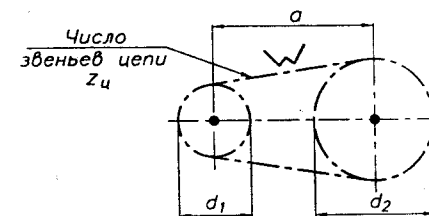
Схема и основные размеры передачи с приводной зубчатой цепью
